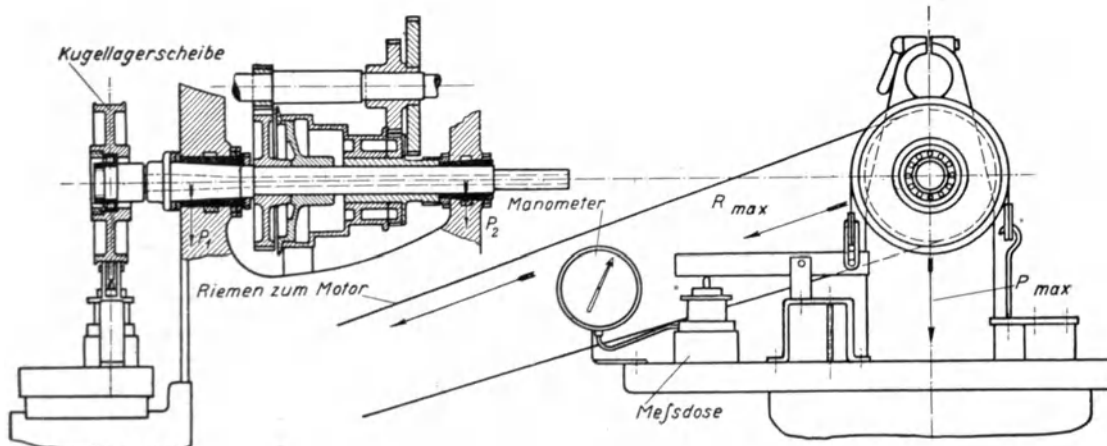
Versuchseinrichtung für die Främaschine Fig. 2.
